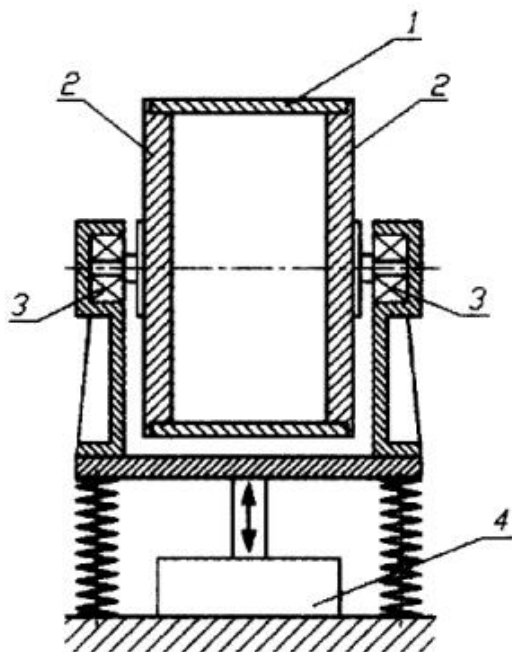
Вибрационный смеситель: 1 – корпус рабочей камеры; 2 – торцевые крышки; 3 – опоры, передающие вибрационное воздействие рабочей камере, 4 – вибропривод
